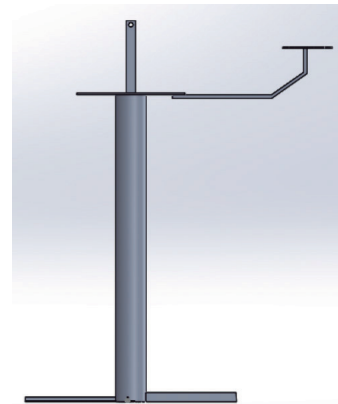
Máquina de soldadura por puntos, vista lateral izquierda.
